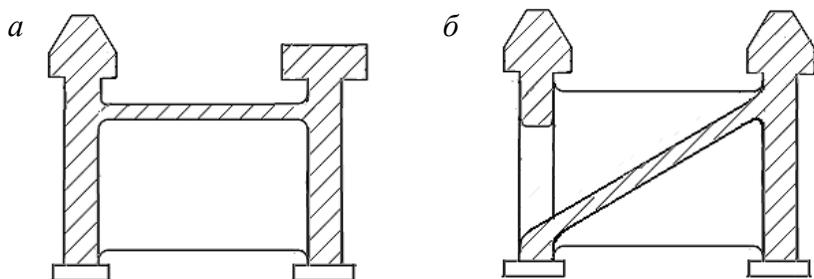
Профили полуоткрытых поперечных сечений станин с горизонтальной (а) и наклонной полками (б)
